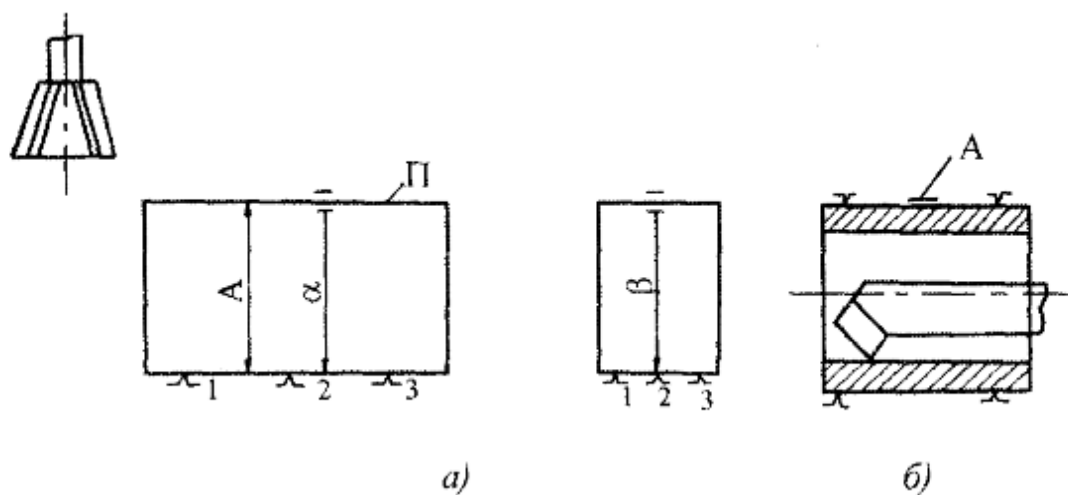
Обробка заготовок при використанні однієї бази:
